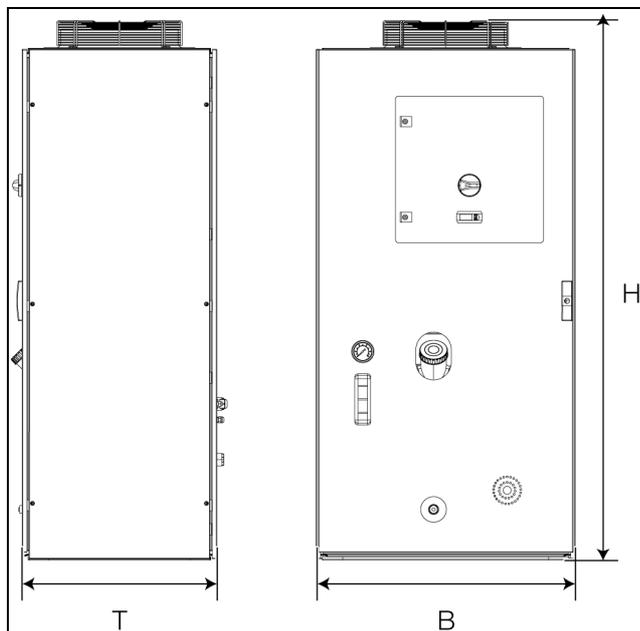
Dimensioni lato anteriore senza zoccolo (in figura 3335.790)
